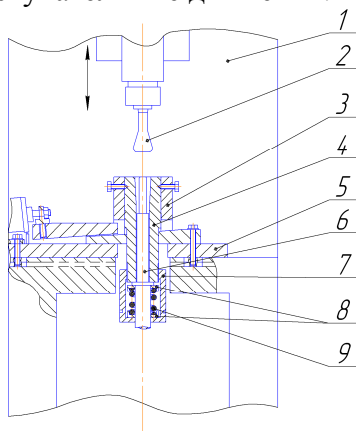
Установка для калибровки конусной части электродов контактной сварки.
